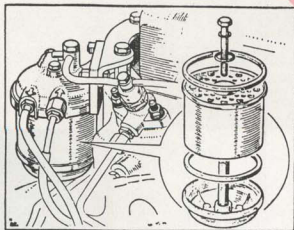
Componentes del filtro principal de combustible, montado en la parte posterior del motor.
